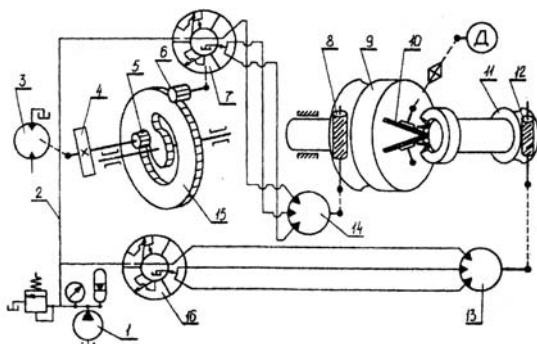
Структурная схема зуборезного станка с гидравлической цепью обката для нарезания прямозубых конических колес
